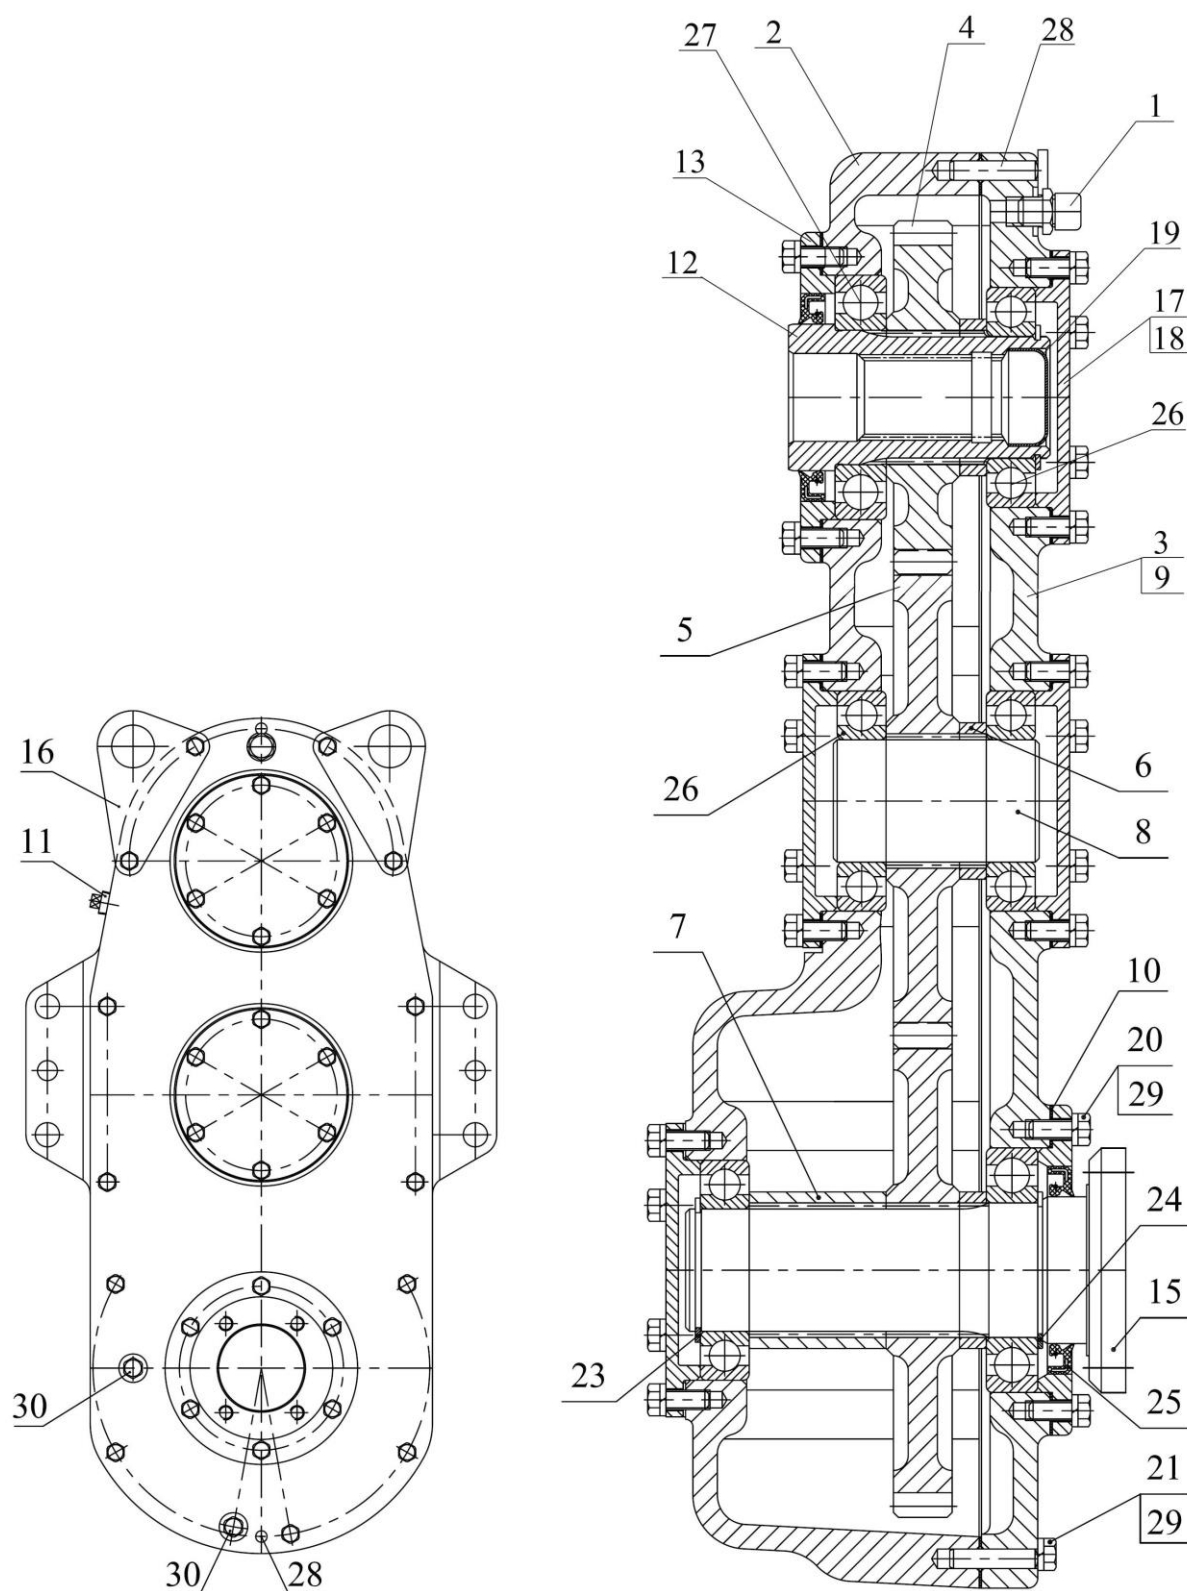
Передний ВМ. Редуктор 2822ДЦ-4209010
